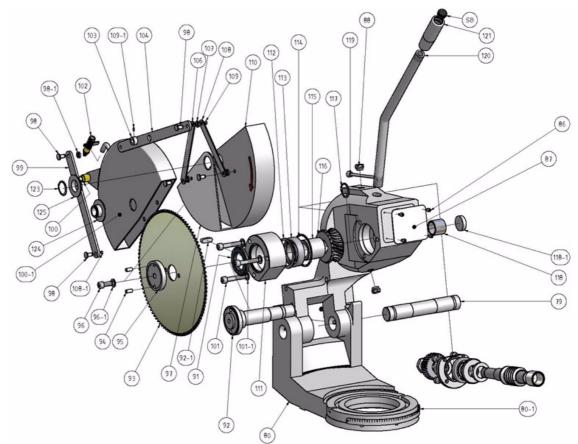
Vorderansicht - Front view - CS275/ CS315
